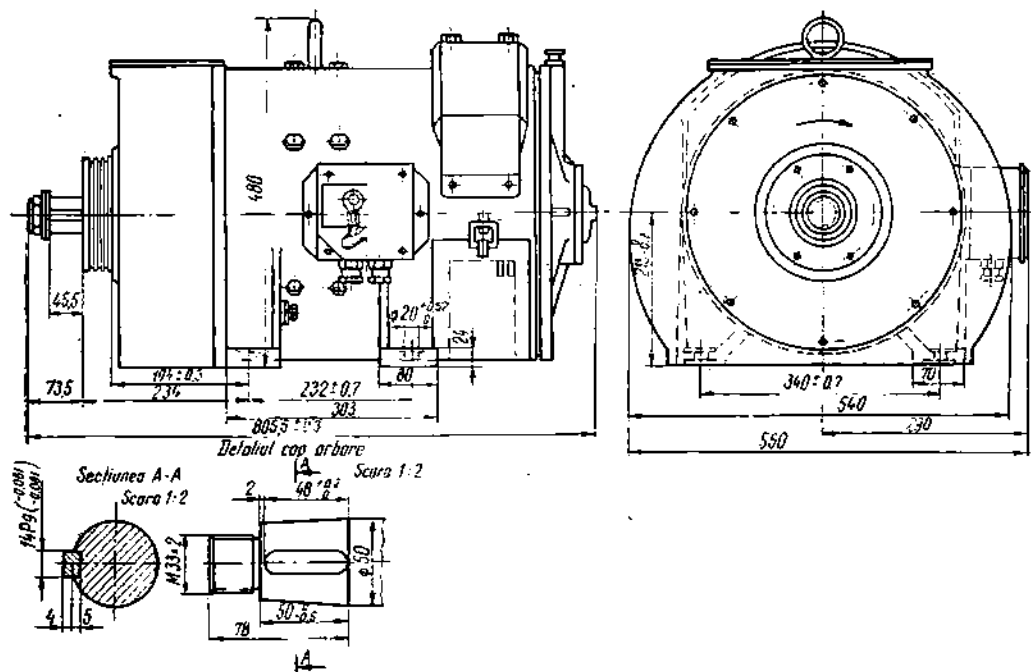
Motor tip 55 a și 55 c. Dimensiuni de montaj.
